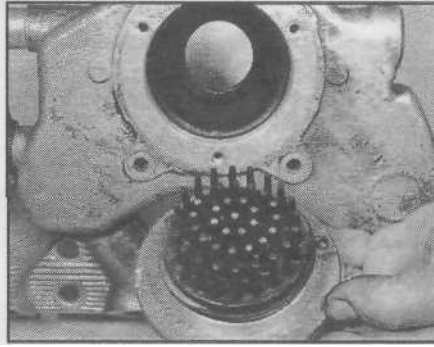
, б. ...и снимите нагревательный элемент с впускного коллектора
